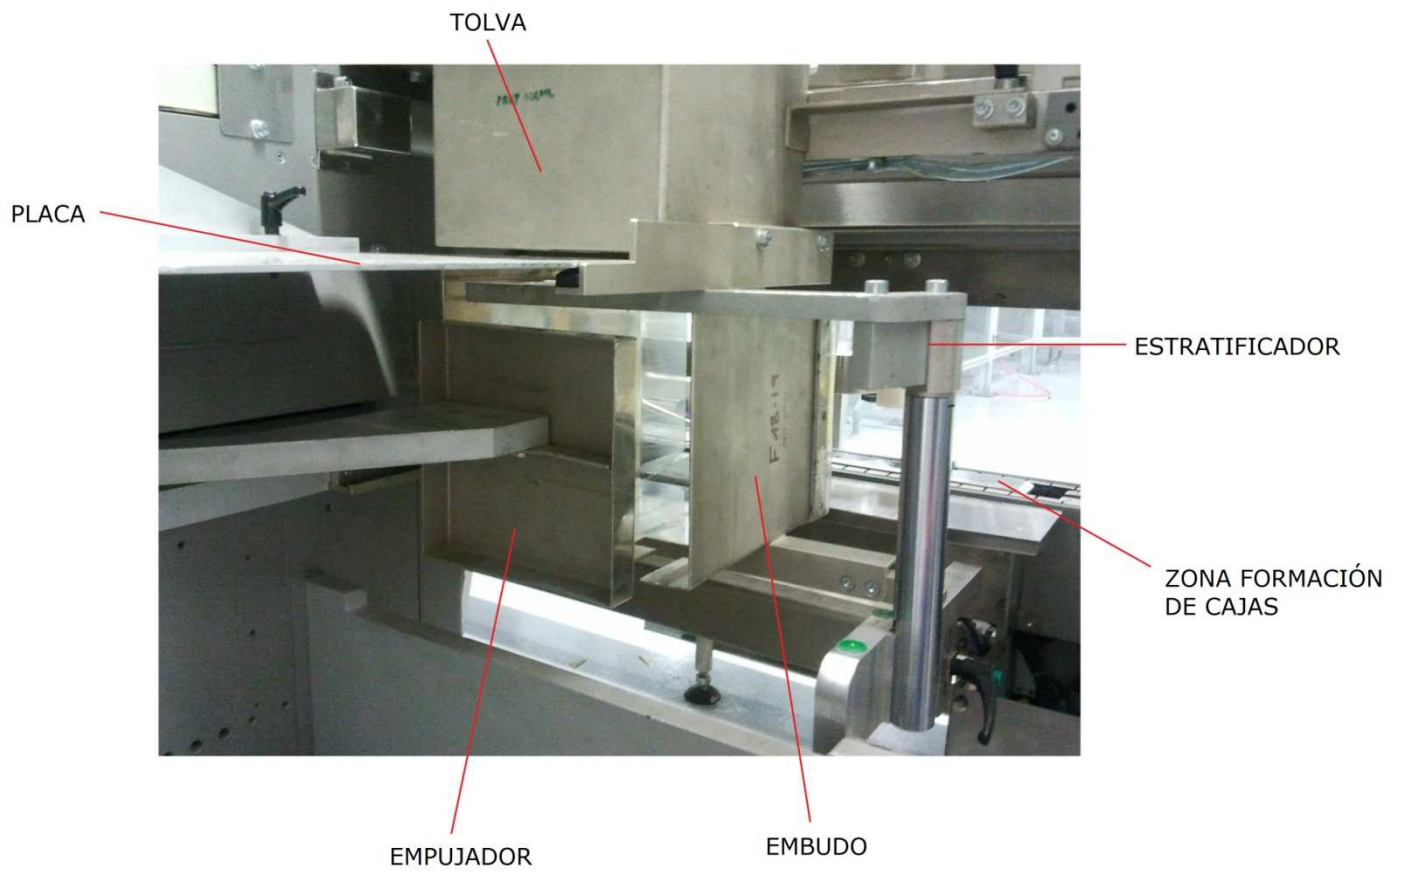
Ilustración de las piezas para la colocación de los estuches.
